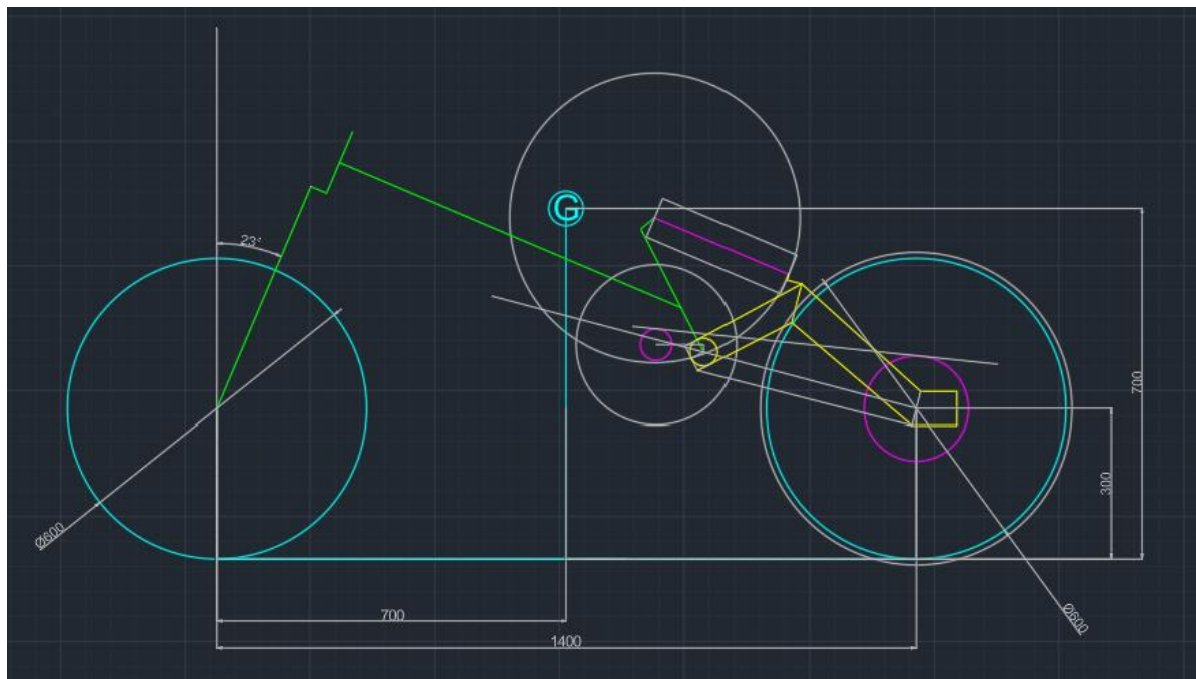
Geometría de la moto. (fuente: ISC Racing Team)
